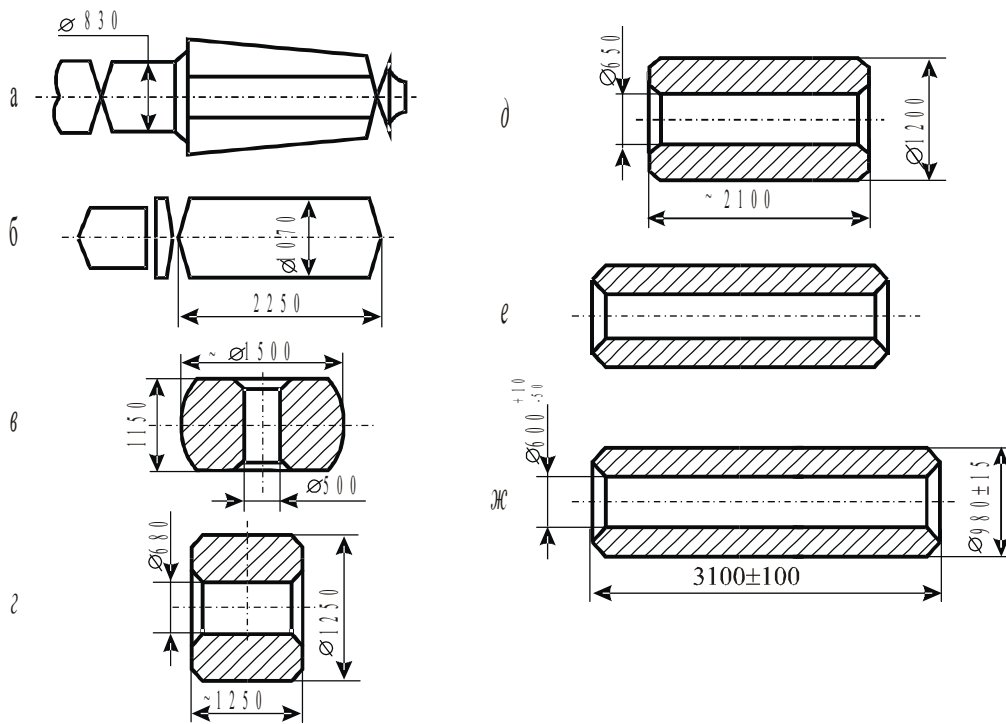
Ковка пустотілого барабану масою 11,6 т з злитку 22 т за шість виносів: а – відтяжка цапфи, відрубка донної частини; б – біллетировка та відрубка прибутку; в – осадка і прошивка дірки діаметром 500 мм; г – розкатка до діаметру 680 мм; д – протяжка на довжину 2100 мм; е – завершальна протяжка до 3100 мм; ж – поковка
